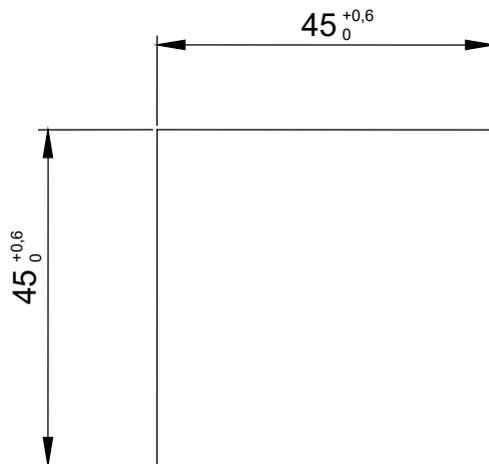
Montageausschnitt für Regler 70304 für Frontplatteneinbau
